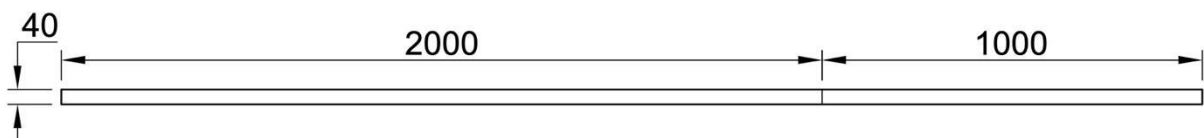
Plan rezanja aluminijskog lima debljine 4 mm
